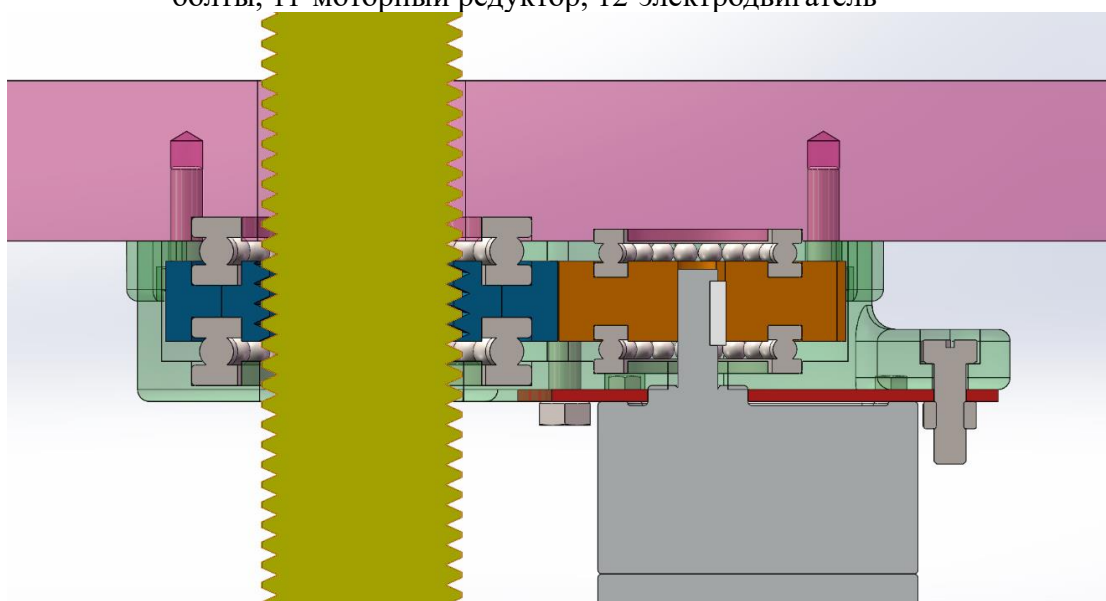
Вид в плане 3D-модели шагового механизма системы управления в SolidWorks
